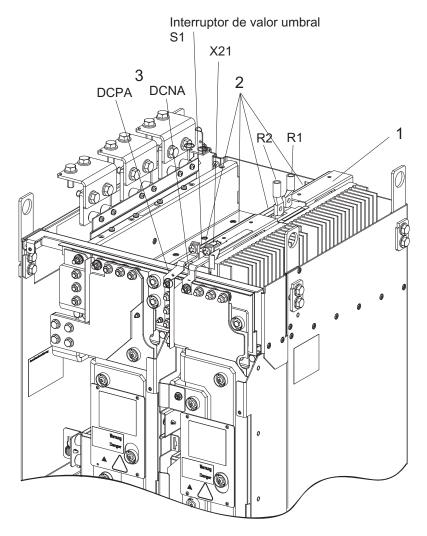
Montaje del Braking Module en un Power Module de tamaño HX
